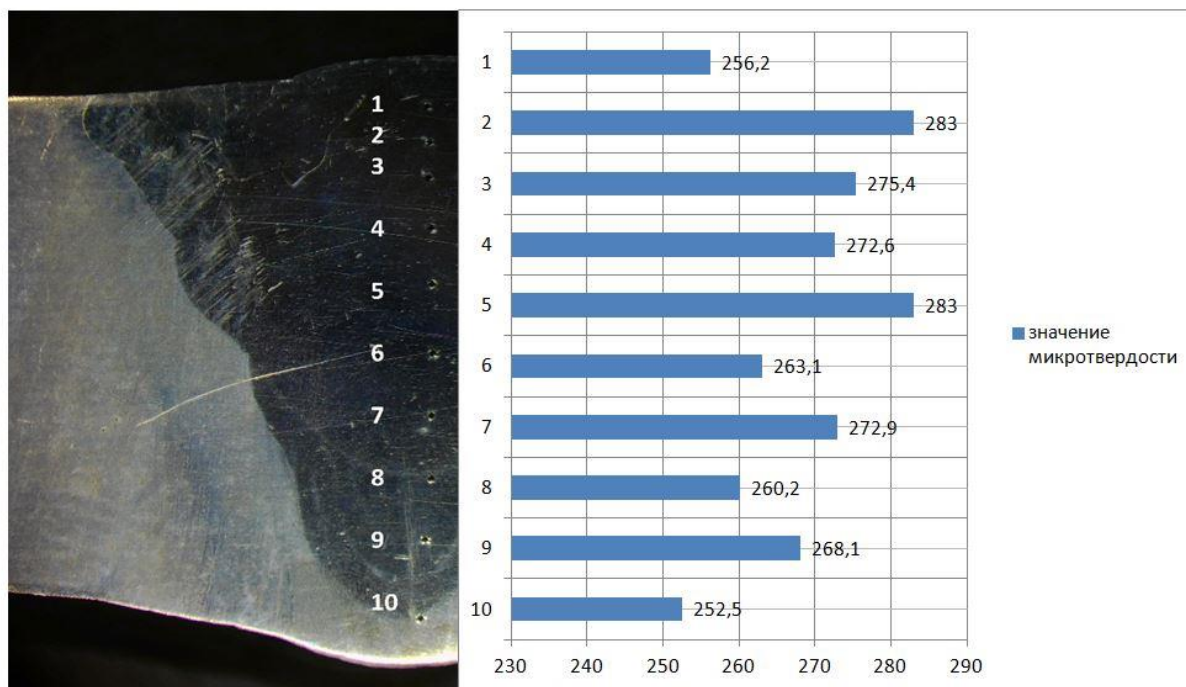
Микротвердость сварного шва образца варианта 1
